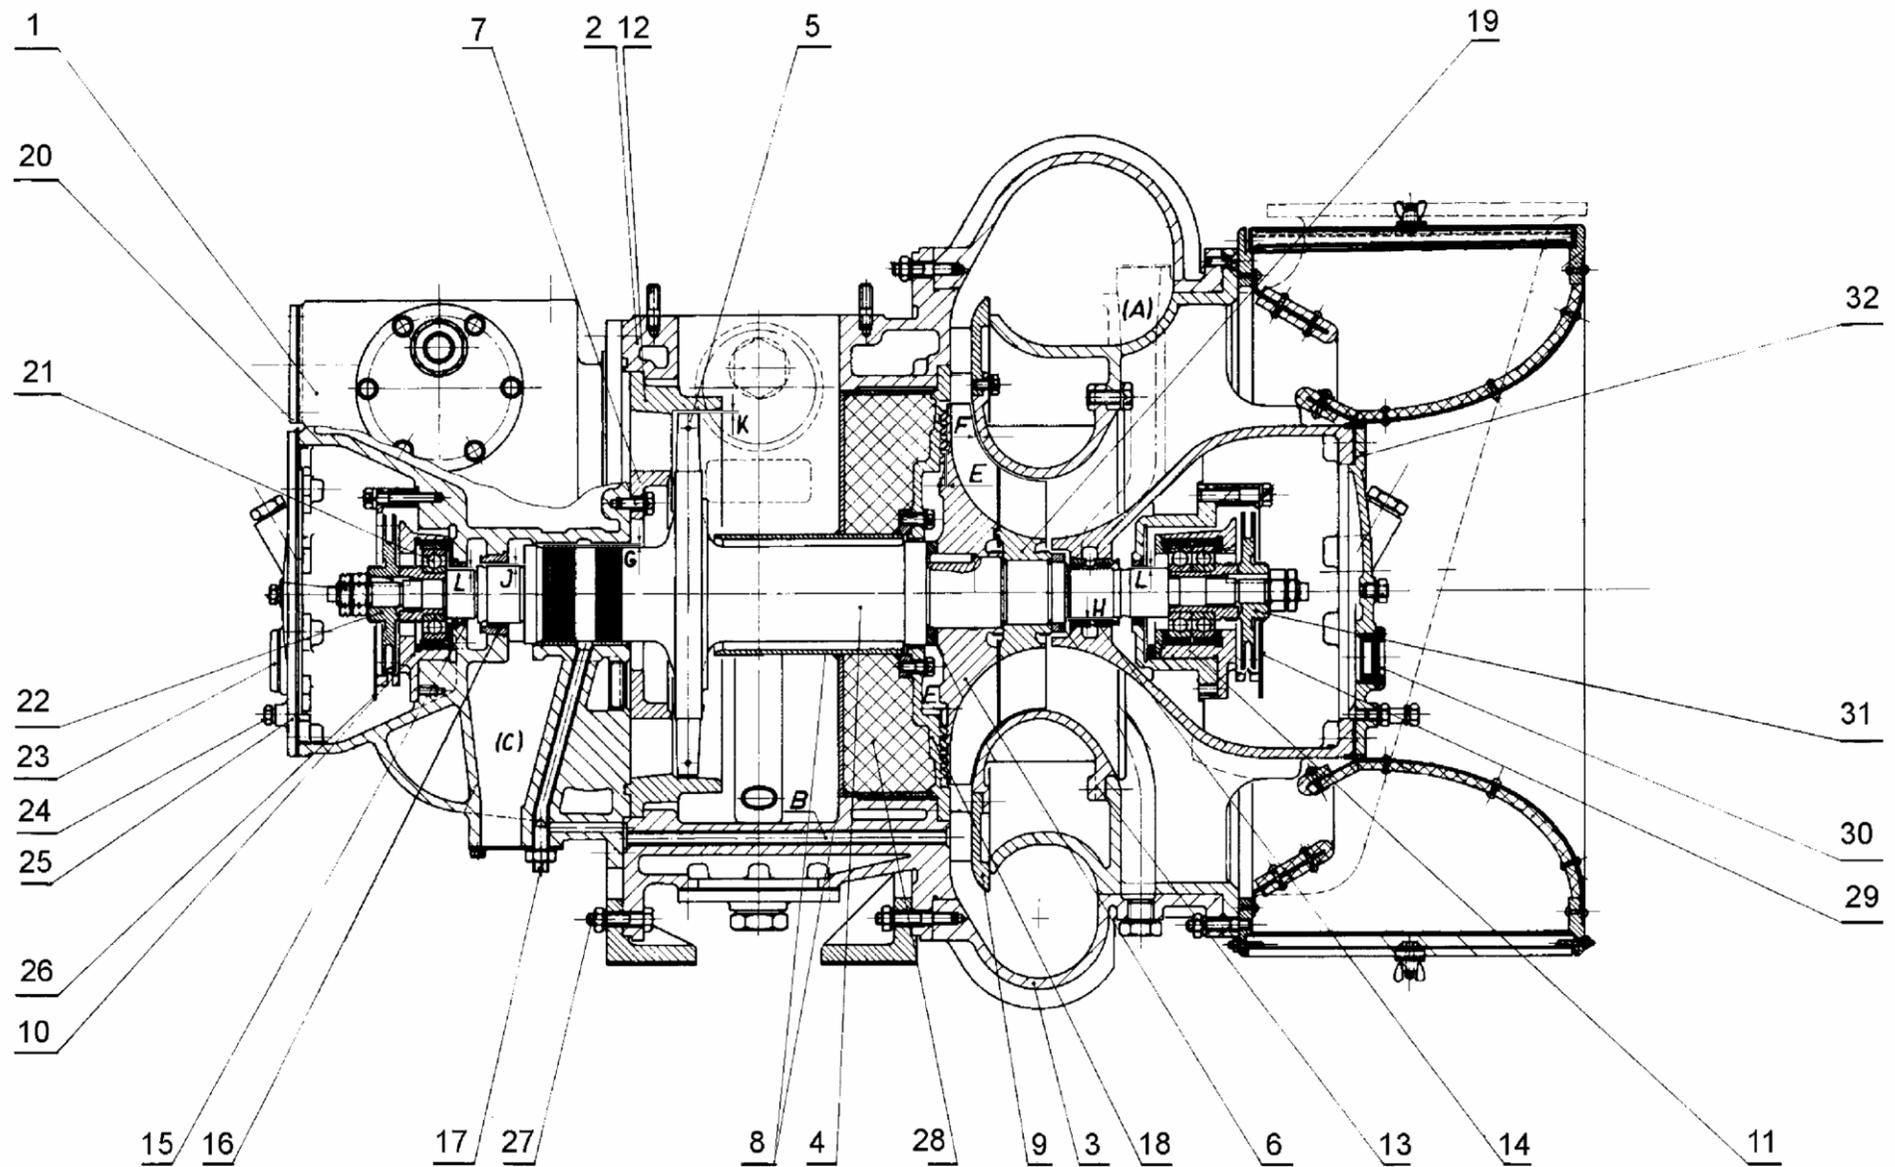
Общий вид турбокомпрессора PDH50 V
